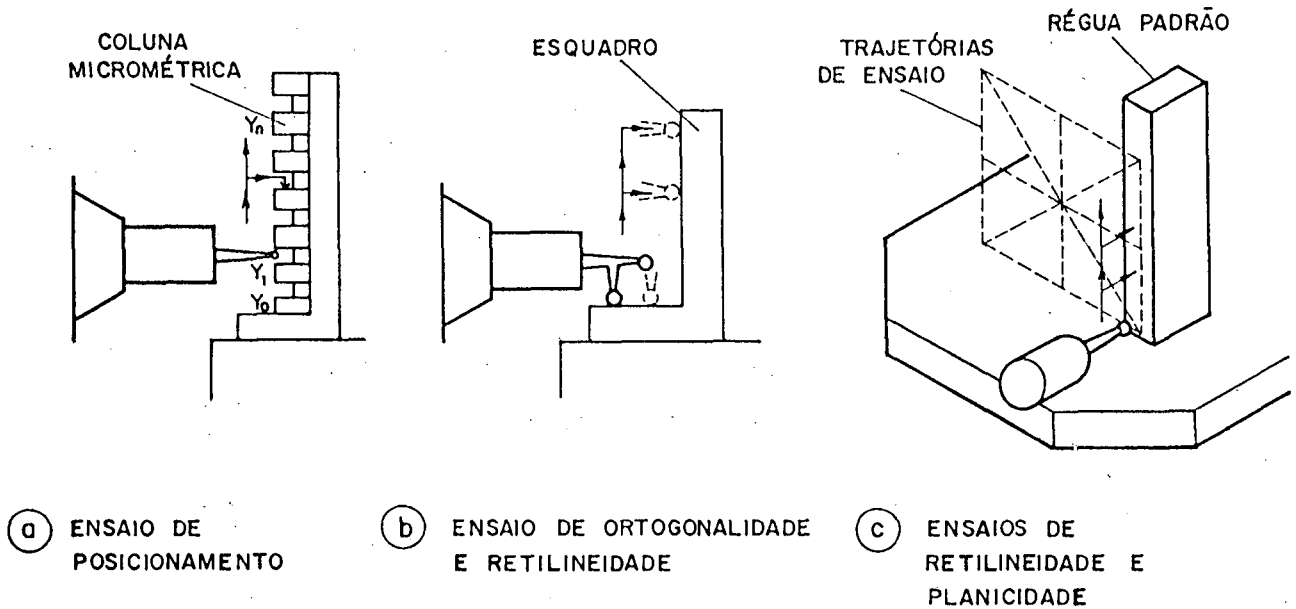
Ensaio geométricos da máquina ferramenta com o SMCP
